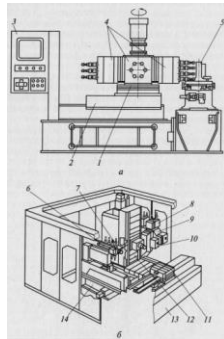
Агрегатні верстати з ЧПК зі змінними шпиндельними коробками (а) і з магазином шпиндельних коробок (б):
